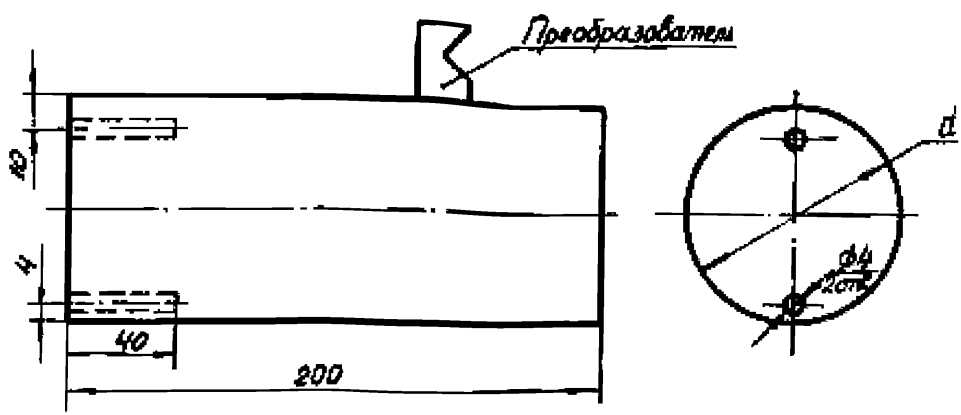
Стандартный образец для настройки ультразвукового прибора при НК штролов;
